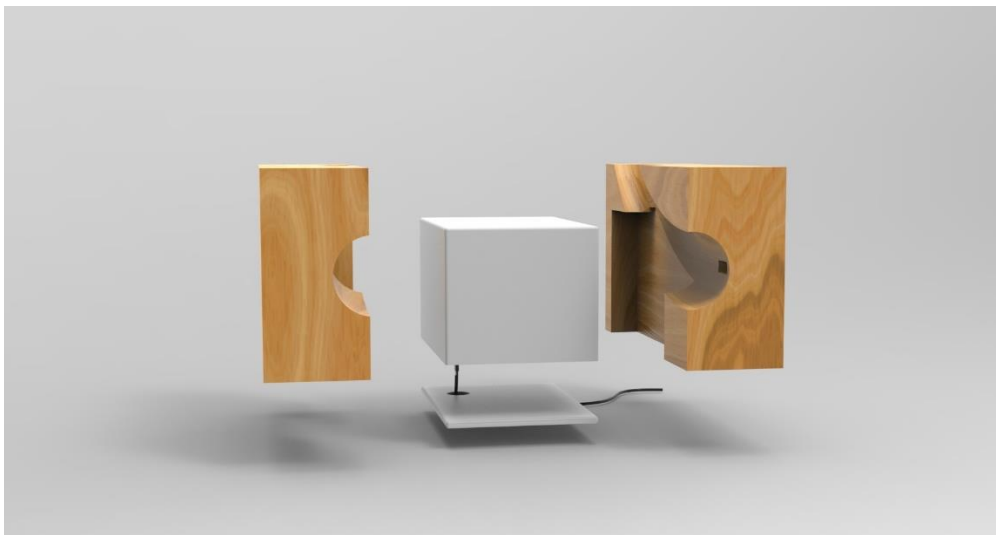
Vnitřní mechanismy a komponenty nástěnného kusu
